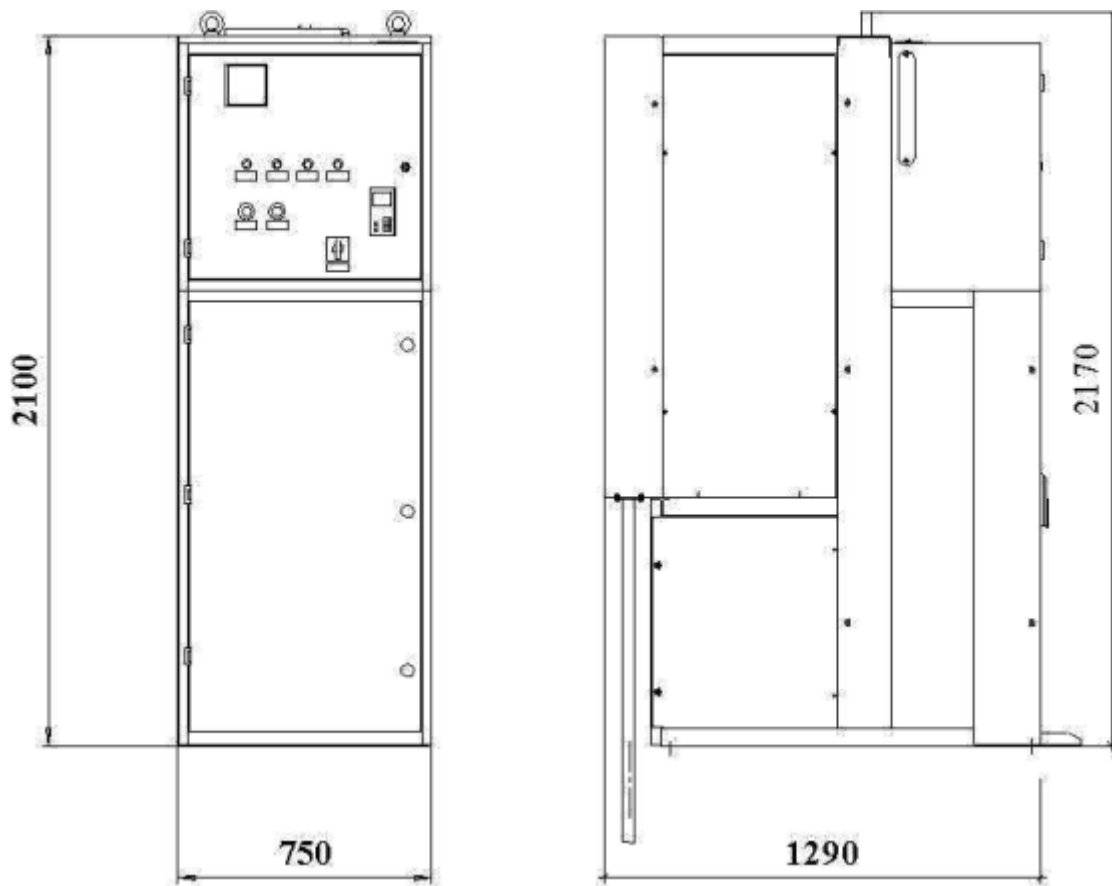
Габаритные размеры камер К-64-МЧ внутренней установки
